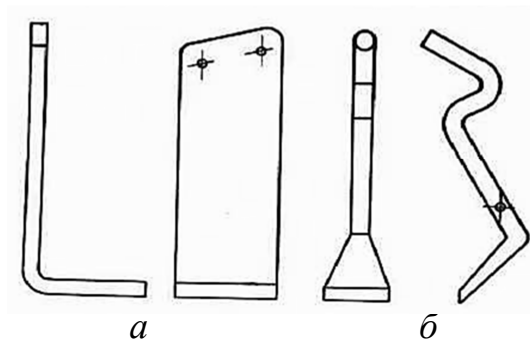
Образцы ножей почвофрез фирмы Говард:
